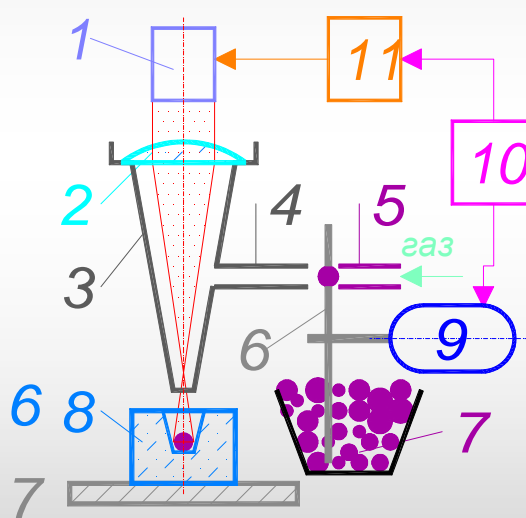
(18.7).ЛТУ для обробки отворів конічної форми
